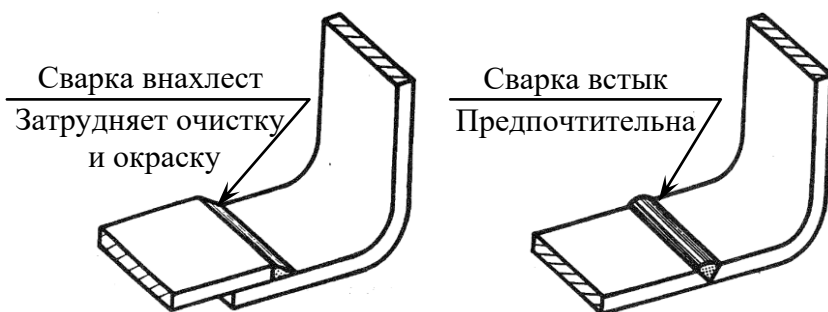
Конструкции сварных соединений (ISO 12944-3).
